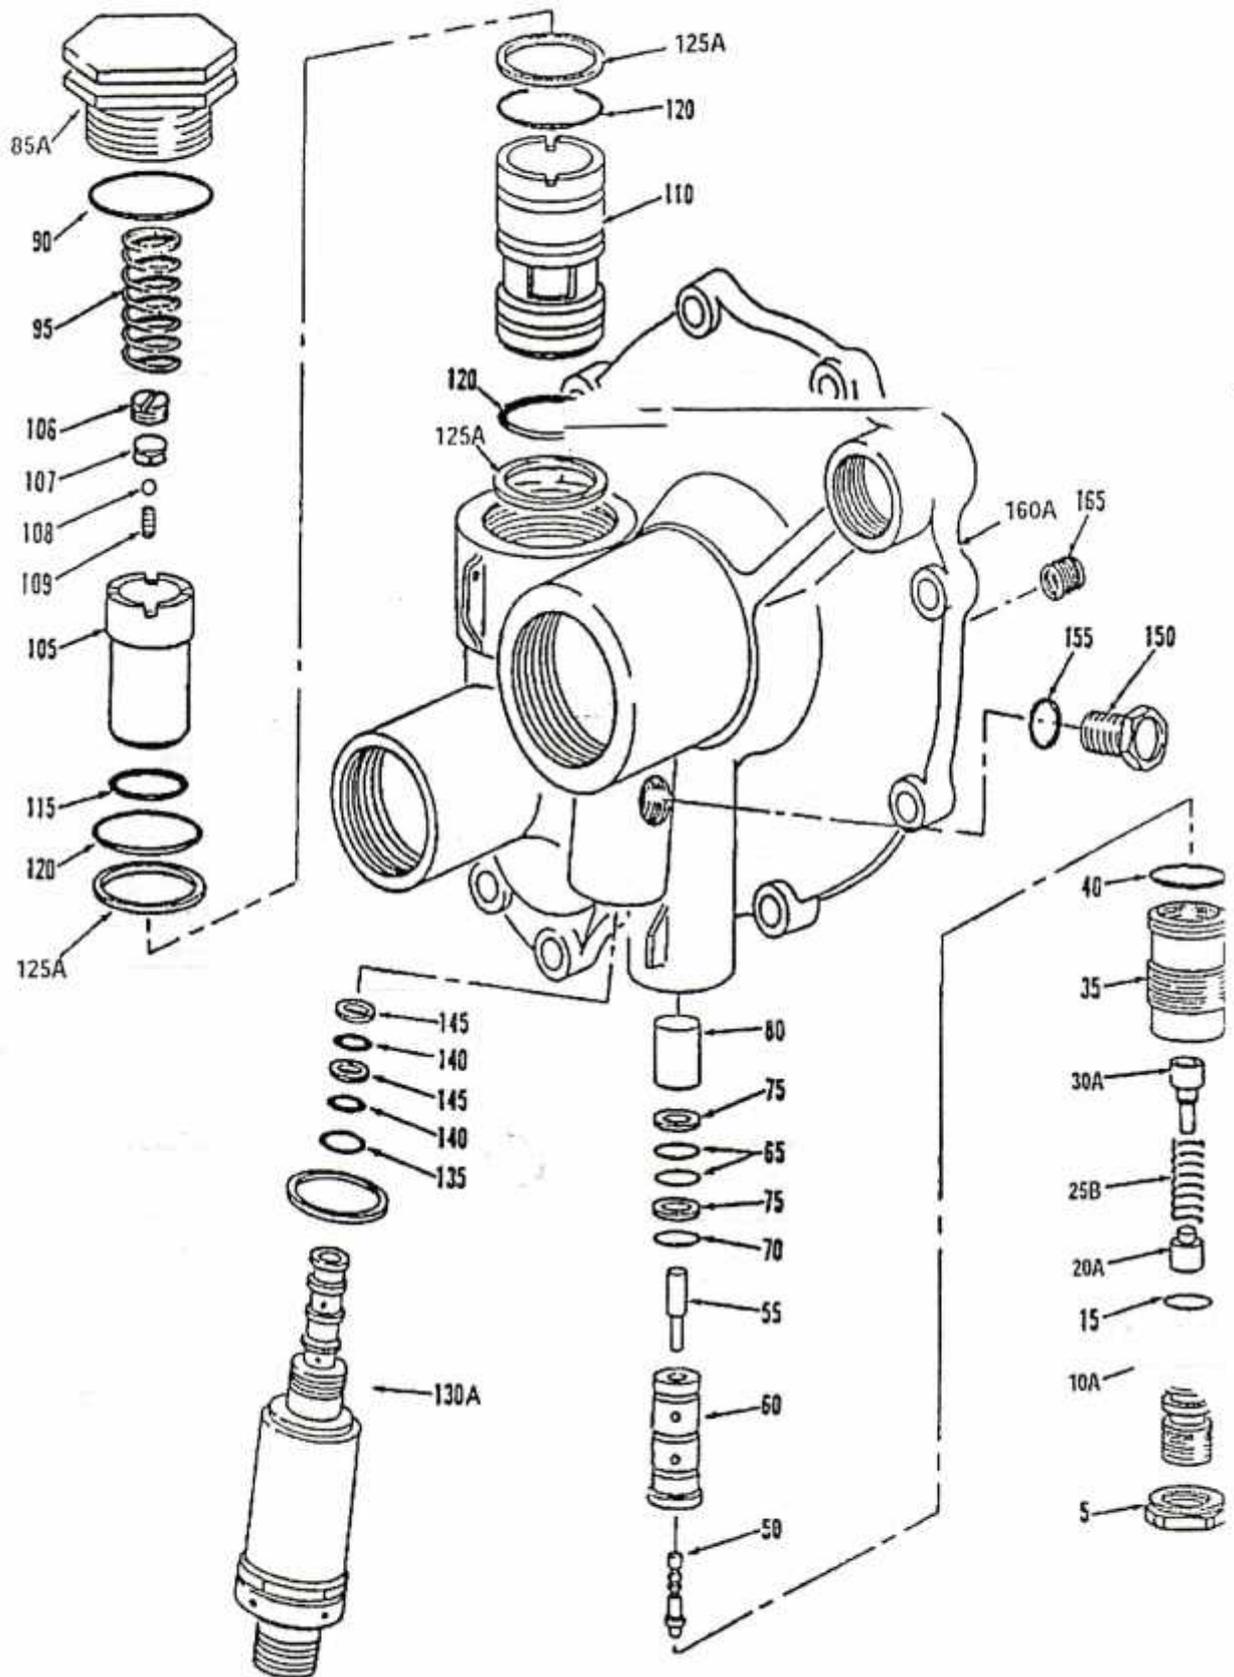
le block valve et les sous ensembles (vue éclaté)
